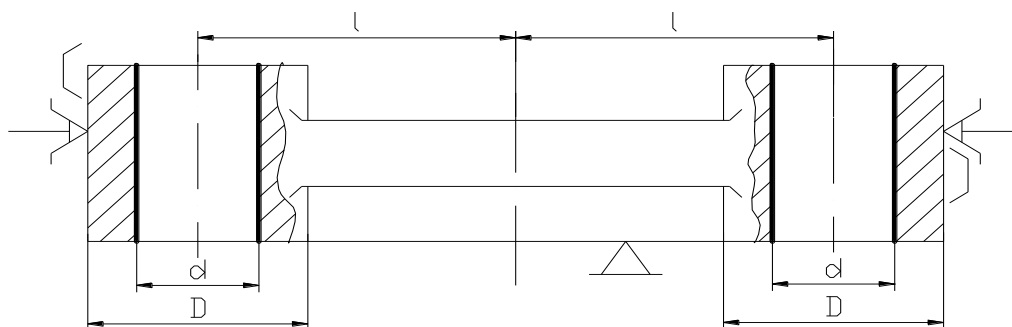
Схема установки заготовки в самоцентрирующих тисках с призматическими губками
